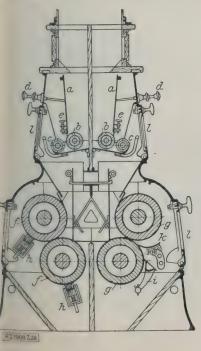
Doppelwalzenstuhl mit schrägliegenden Walzen.
